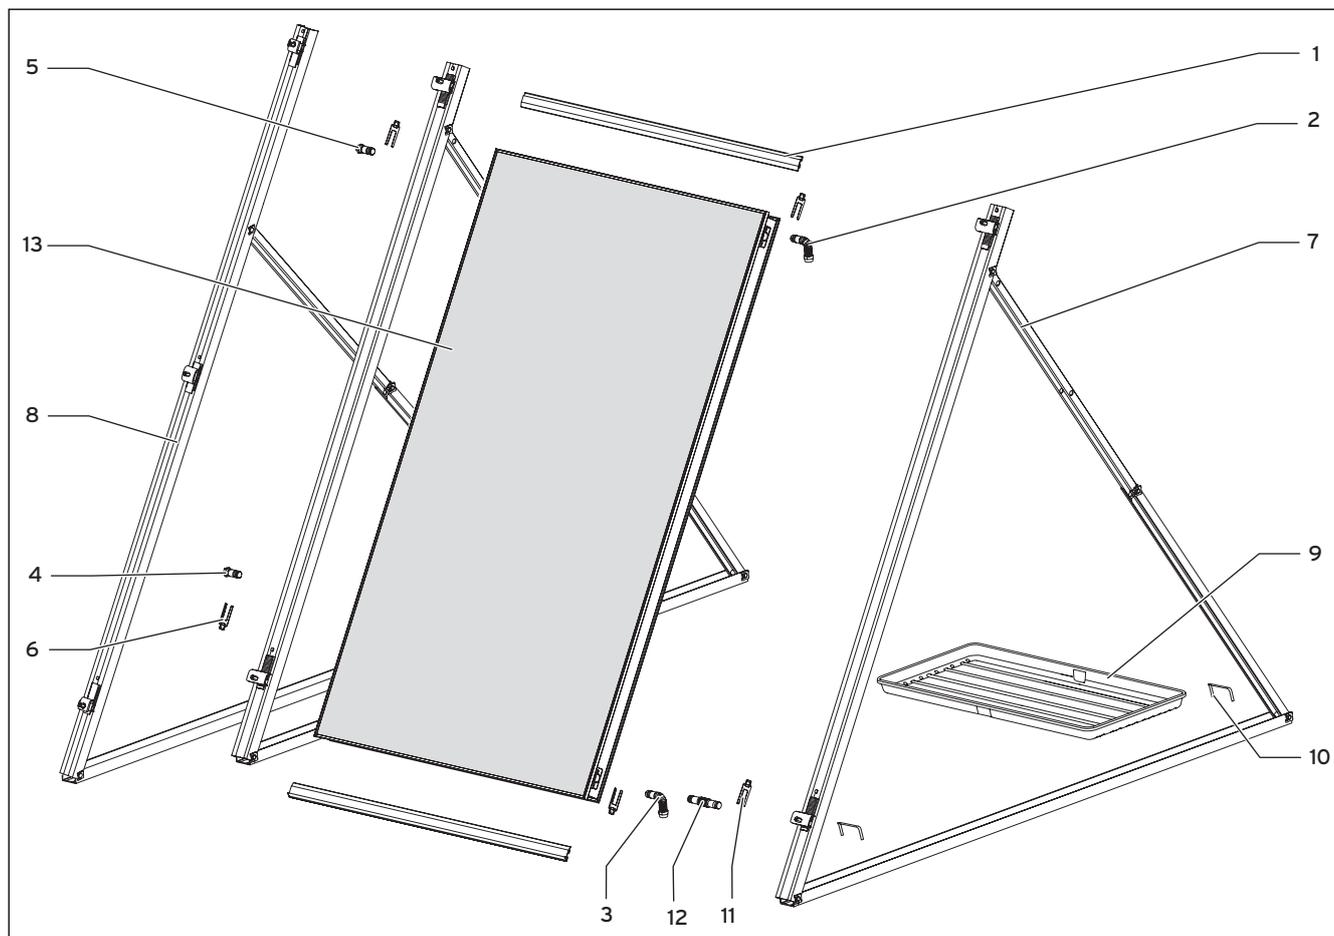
Kit per montaggio su tetto piano (nella figura: collettore verticale)
